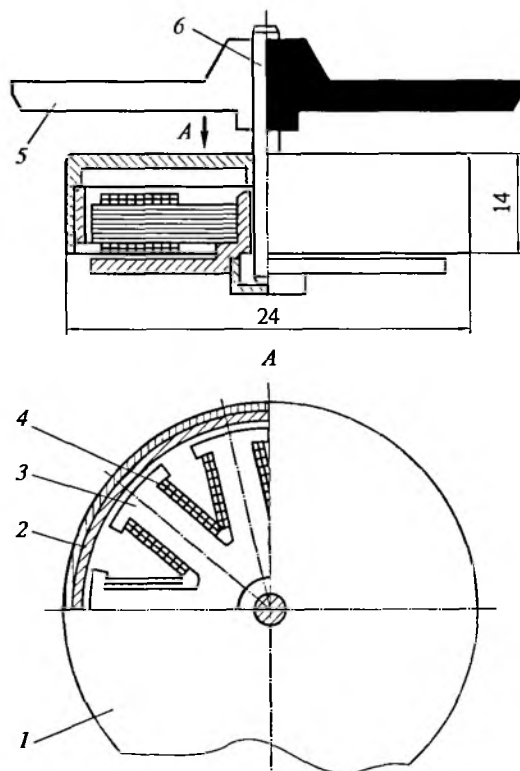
Синхронный двигатель для вращения лазерного диска:
